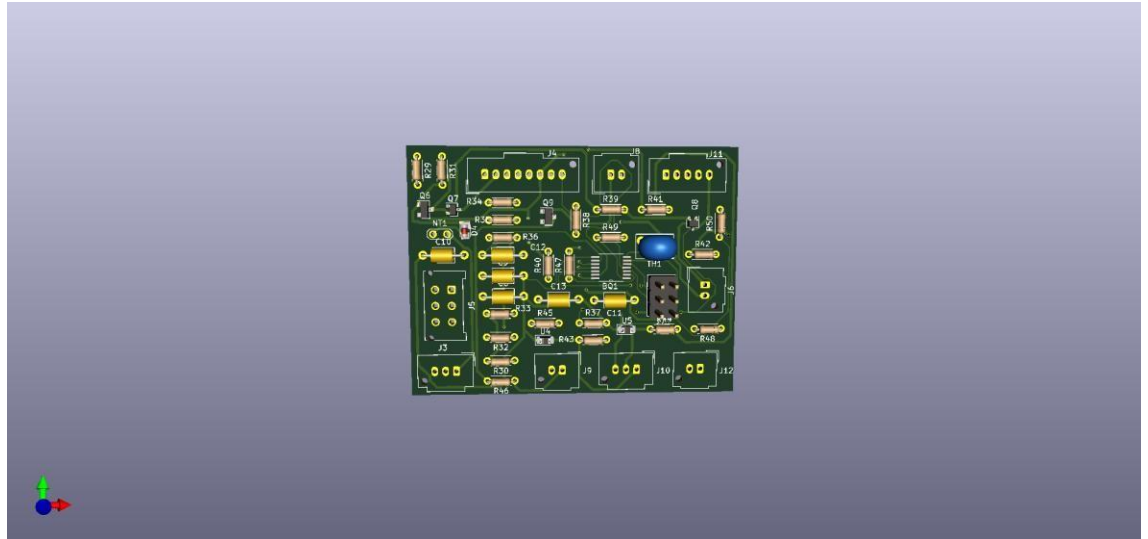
Visión en 3D de la PCB del Fuel Gauge
